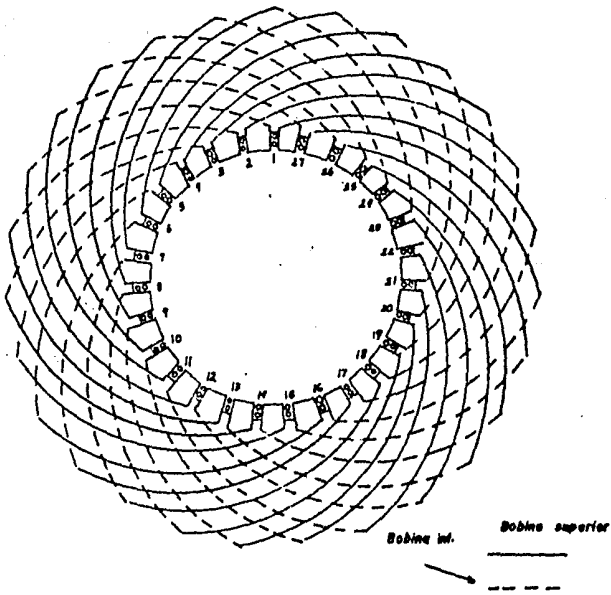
DEVANADO DEL ESTATOR VISTO DEL LADO DE LA TURBINA
